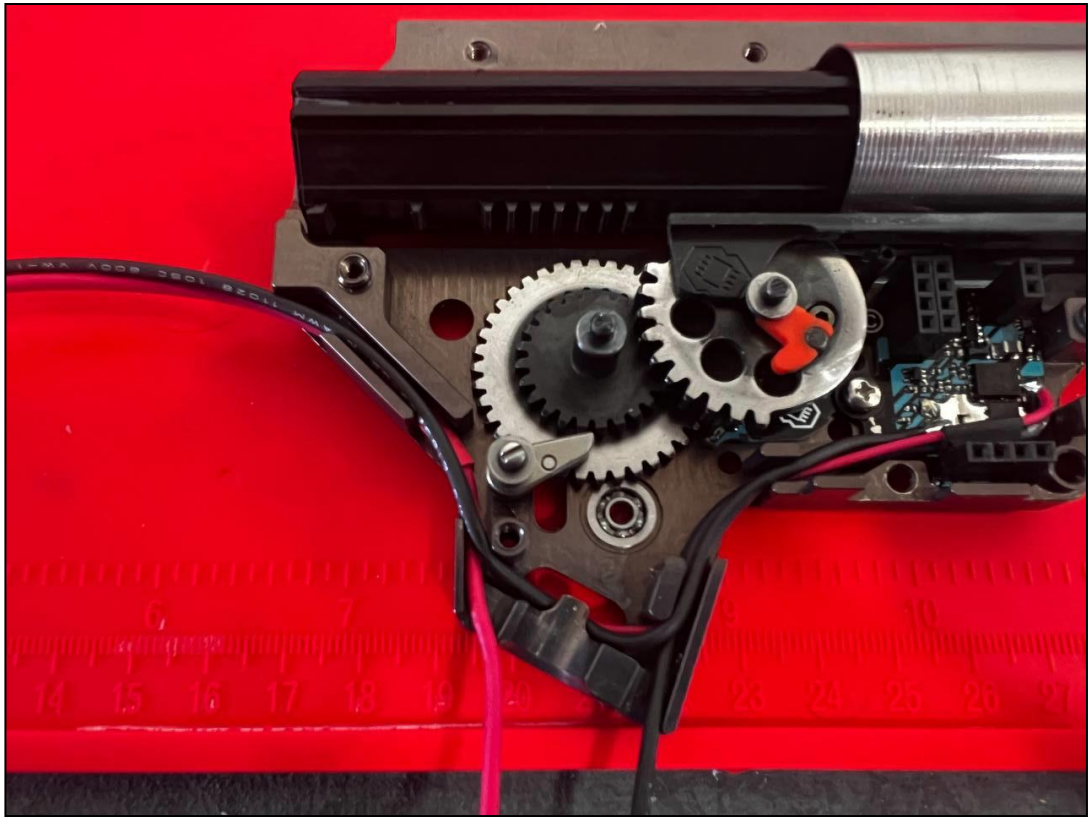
Apertura del Gearbox del proyecto donde se aprecia la parte del proceso de transmisión de movimiento entre engranajes y pistón (Producción propia)
